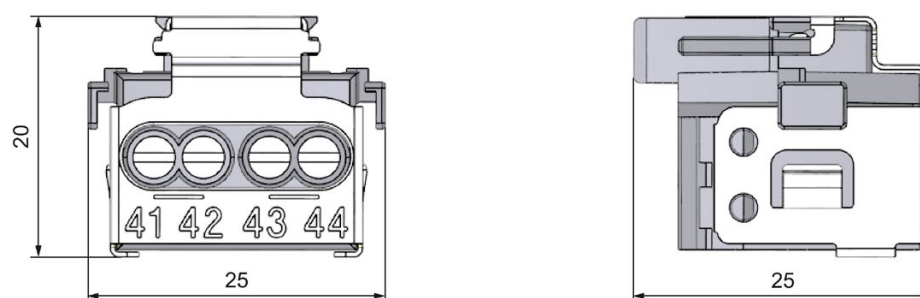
Maßbild Einspeiseelement für 35 mm-Module
